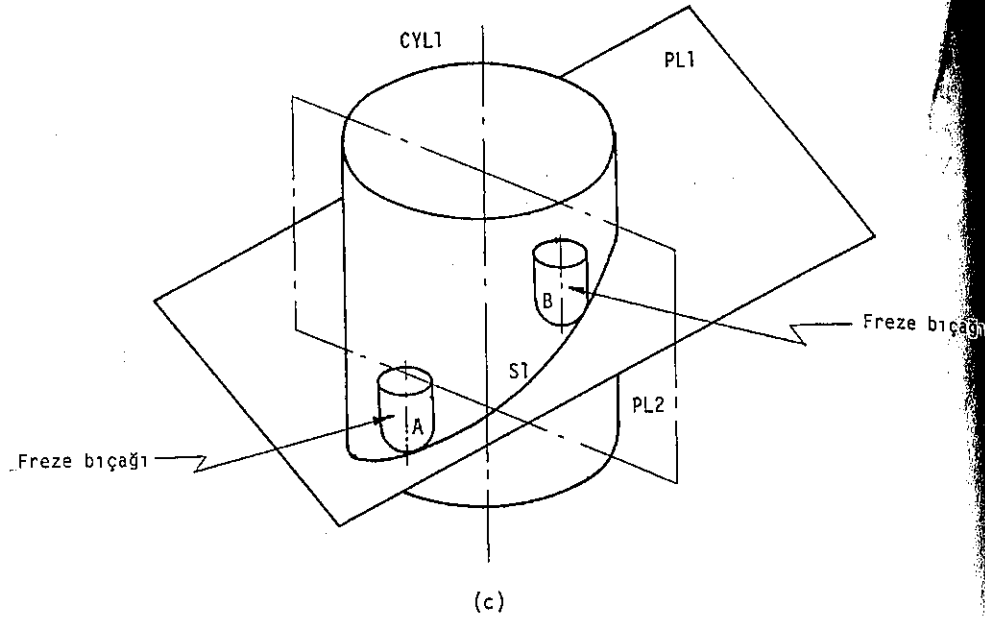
(c)'de, kesici takımın, PL1 düzlemiyle CYL1 silindirinin arakesi-
